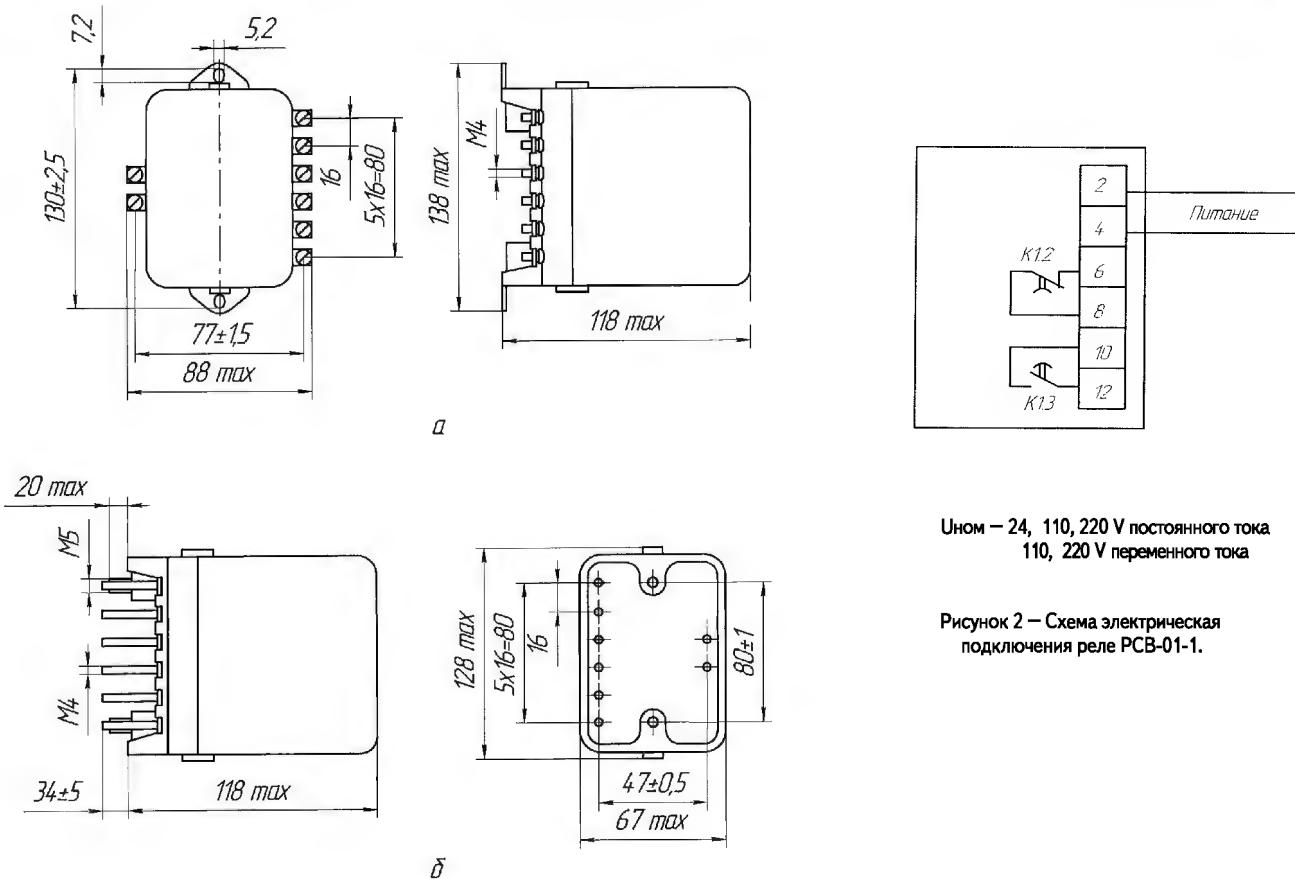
Габаритные, установочные и присоединительные размеры реле типа PCB-01-1, PCB-01-4.
